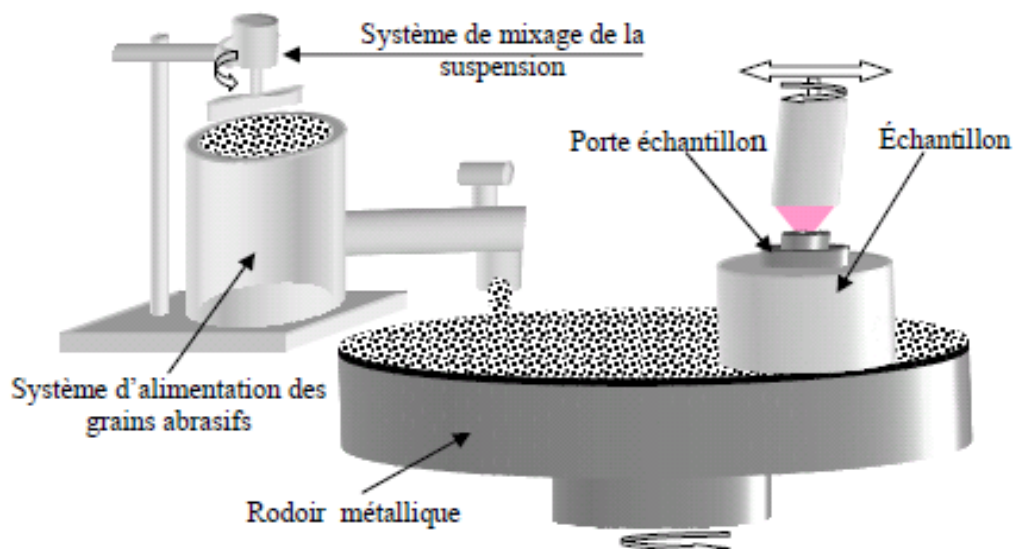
Principe de doucissage par abrasifs libres du verre
